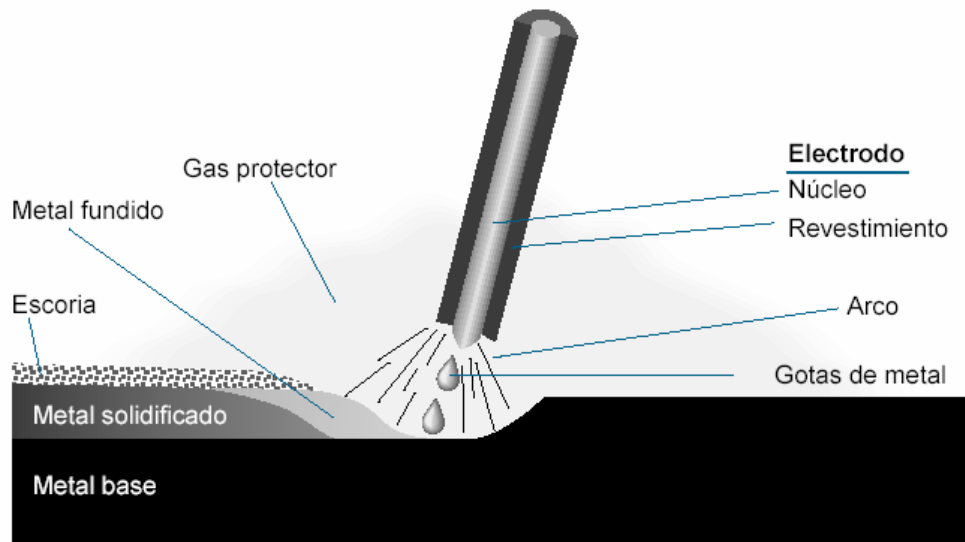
Soldadura metálica con arco protegido (SMAW)
